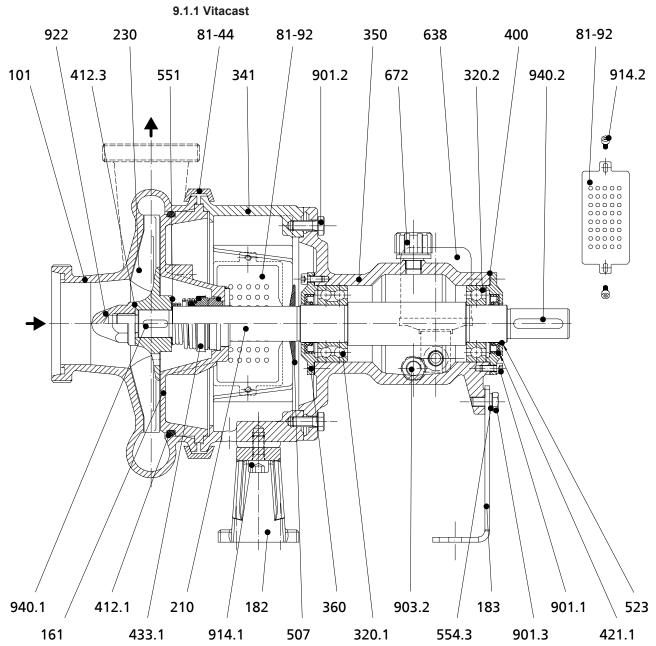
Сборочный чертеж, диаметр вала 28 мм, 43 мм
